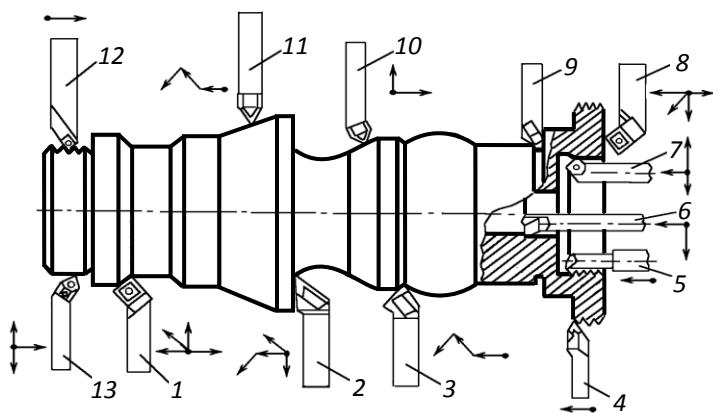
Схема обробки основних типових поверхонь токарними різцями зі змінними багатогранними пластинами
